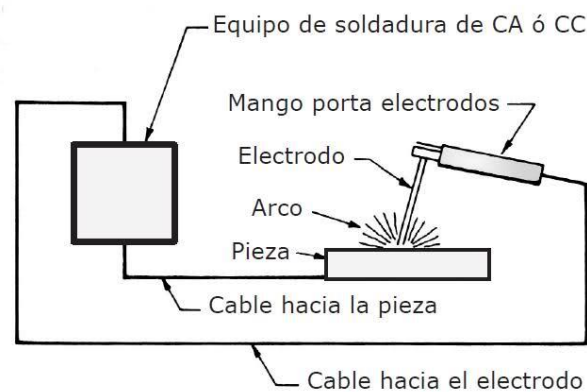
12. Circuito básico de soldadura por arco.
